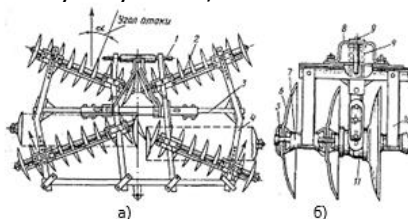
Дисковая борона БДН-3: а – общий вид бороны; б – часть батареи бороны; 1 – навеска; 2 – батарея; 3 – рама; 4 – боковой брус; 5 – ось; 6 – диск диаметром 450...510 мм 7 – шпилька; 8 – кронштейн; 9 – штырь; 10 – чистик; 11 – подшипник
